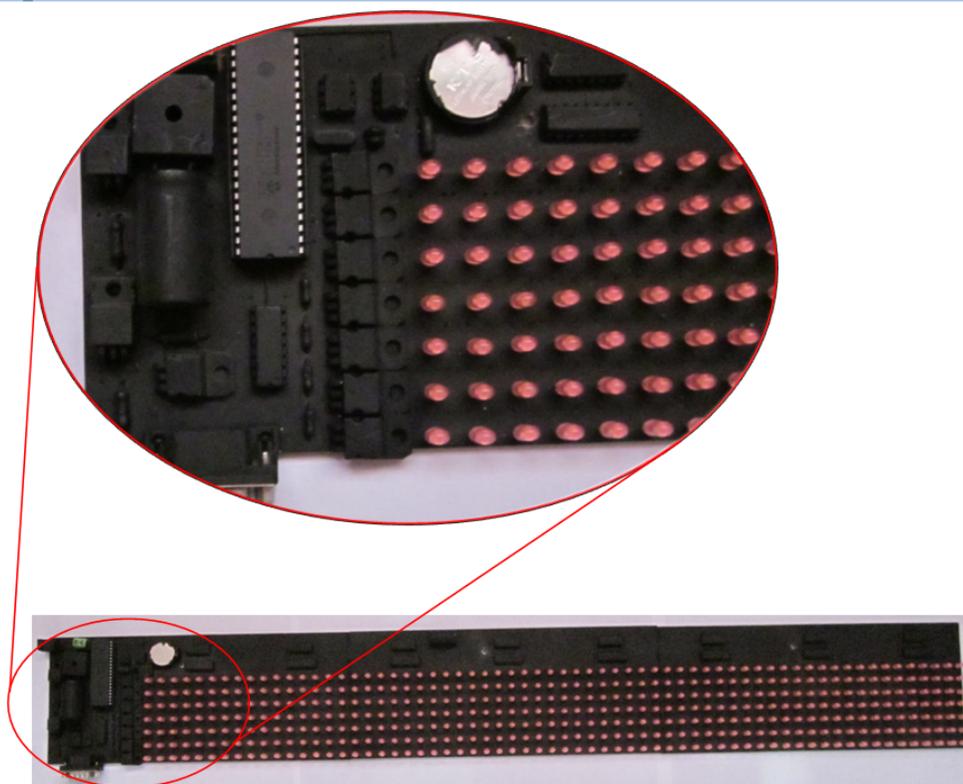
Proceso de soldadura de elementos en la baquelita (anverso)
